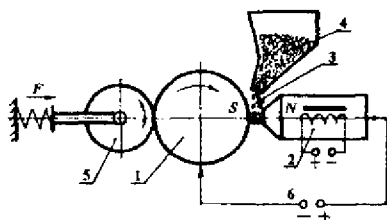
Принципиальная схема комбинированных способов обработки в электромагнитном поле: 1 – заготовка; 2 – электромагнит; 3 – ферромагнитный порошок; 4 – бункер-дозатор; 5 – абразивный круг или деформирующий ролик; 6 – источник разрядного тока
